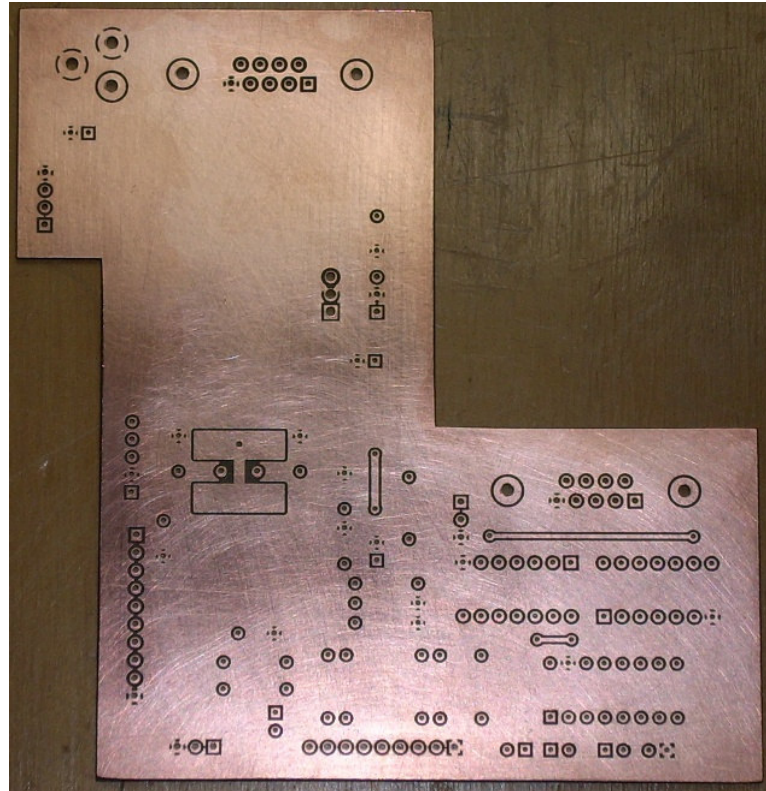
Face inferior da placa de circuito impresso do Módulo Cadastramento
